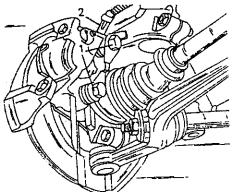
Крепление тормозного суппорта на поворотном кулаке. Стрелками (1) указаны болты крепления. В месте (2) показано крепление тормозного шланга.
